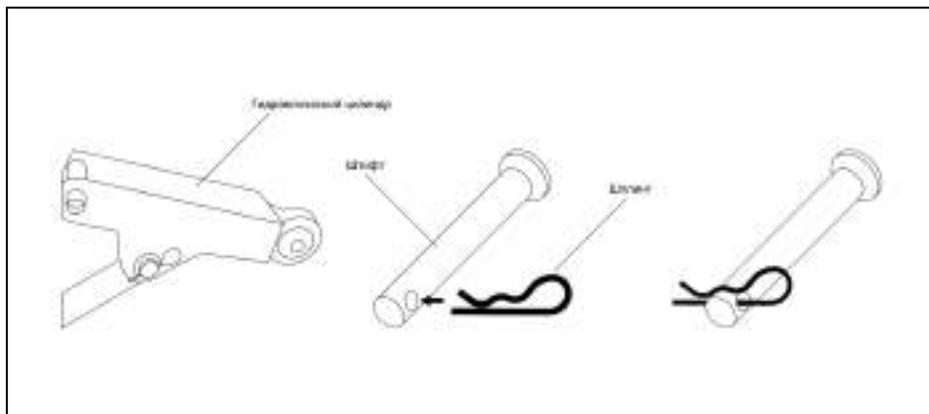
Гидравлический цилиндр, шплинт и штифт
